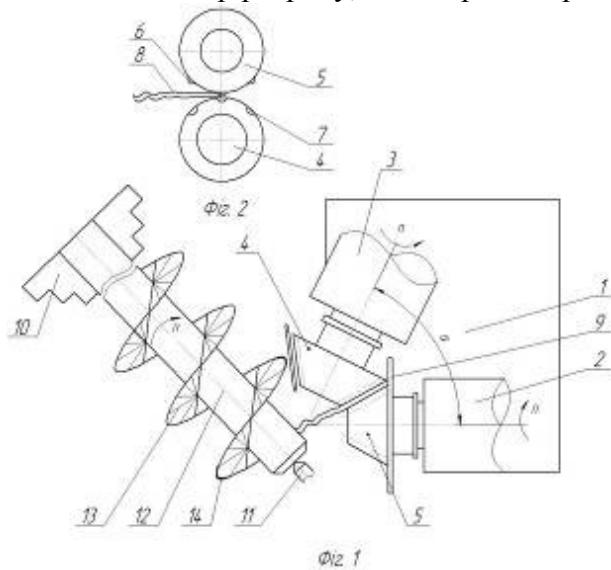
Обкатний верстат для виготовлення гвинтових гофрованих заготовок
